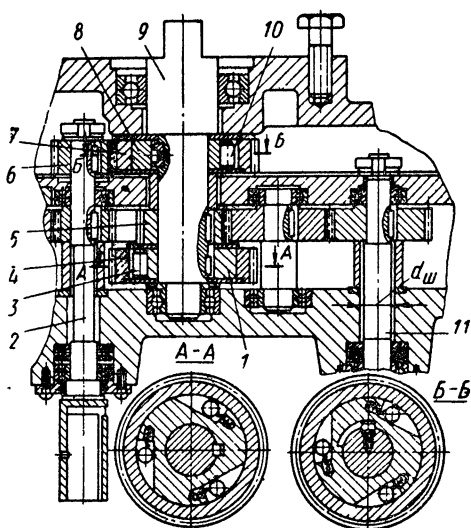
Головка для последовательного сверления и нарезания резьбы
